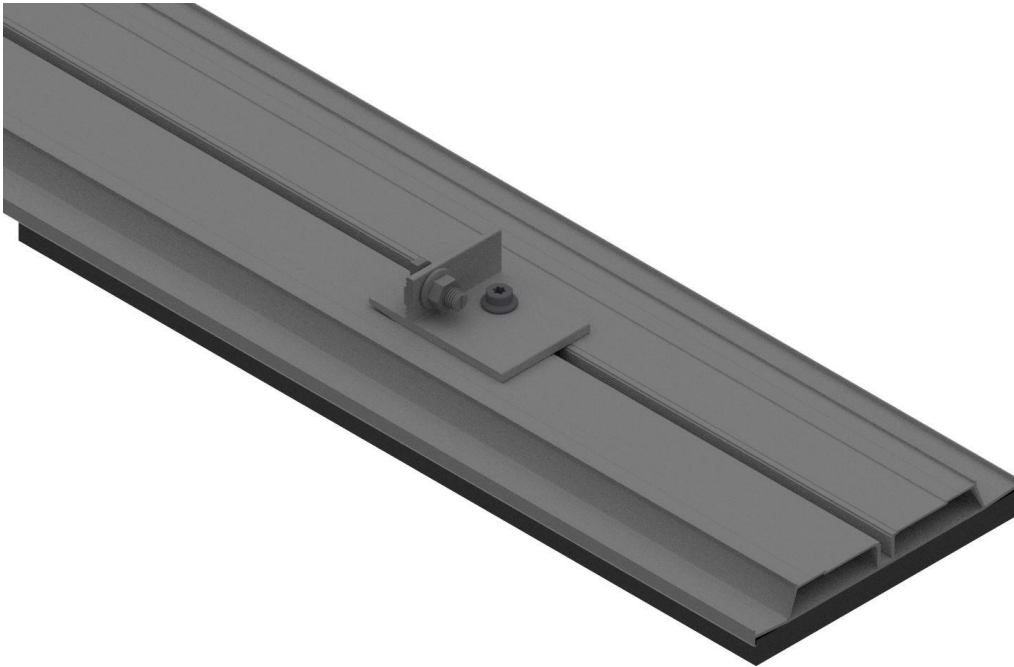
Universalverbinder AeroFlat mit M8x20 Zylinderschraube befestigen
